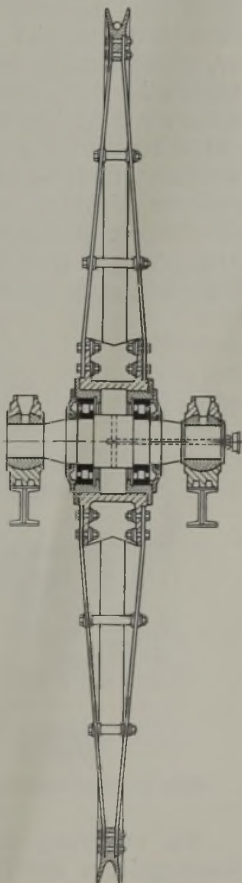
Seilscheibe mit Zylinderrollenlagern.
